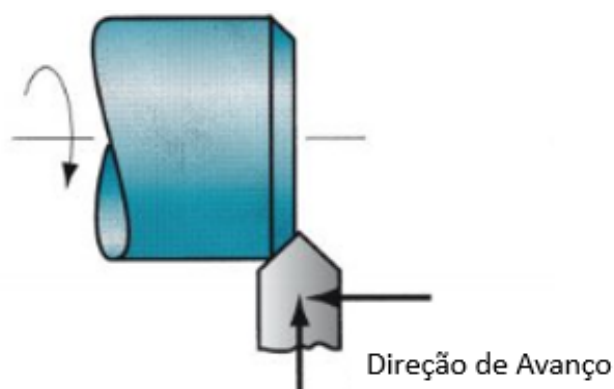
Torneamento cilíndrico (GROOVER, 2014)
